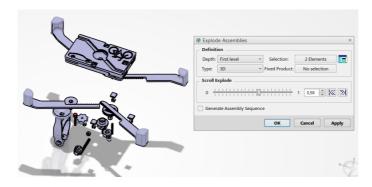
Explosionado 3D, al primer nivel de profundidad.
